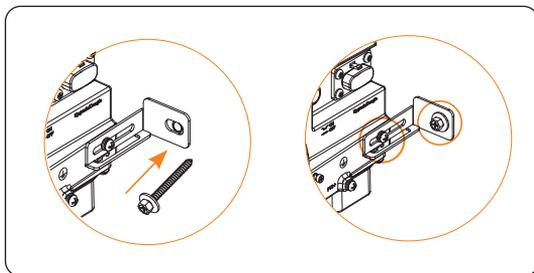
Die Blechschraube auf der rechten Seite und die Schraube M5*10 sichern
